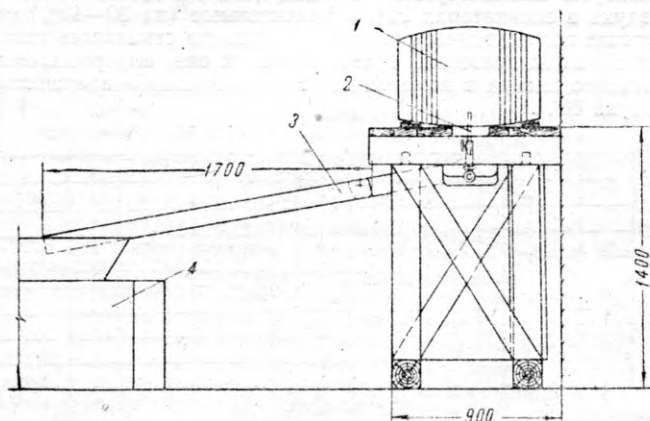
Схема приспособления для выплавки петролатума из бочек острым паром:
